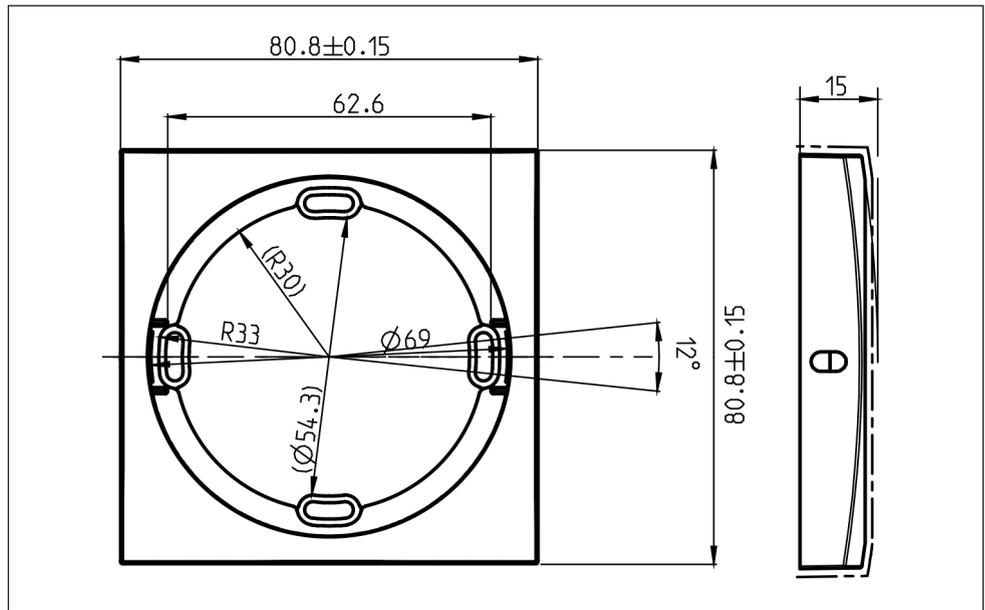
Fiche technique du cadre (vue de dessus et vue latérale)
